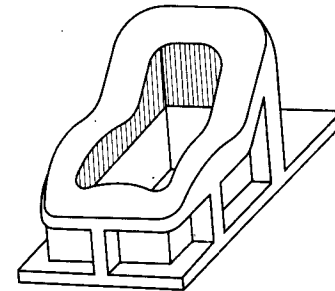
Пример конструкции цельнолитой матрицы штампа для вытяжки крупногабаритной детали
